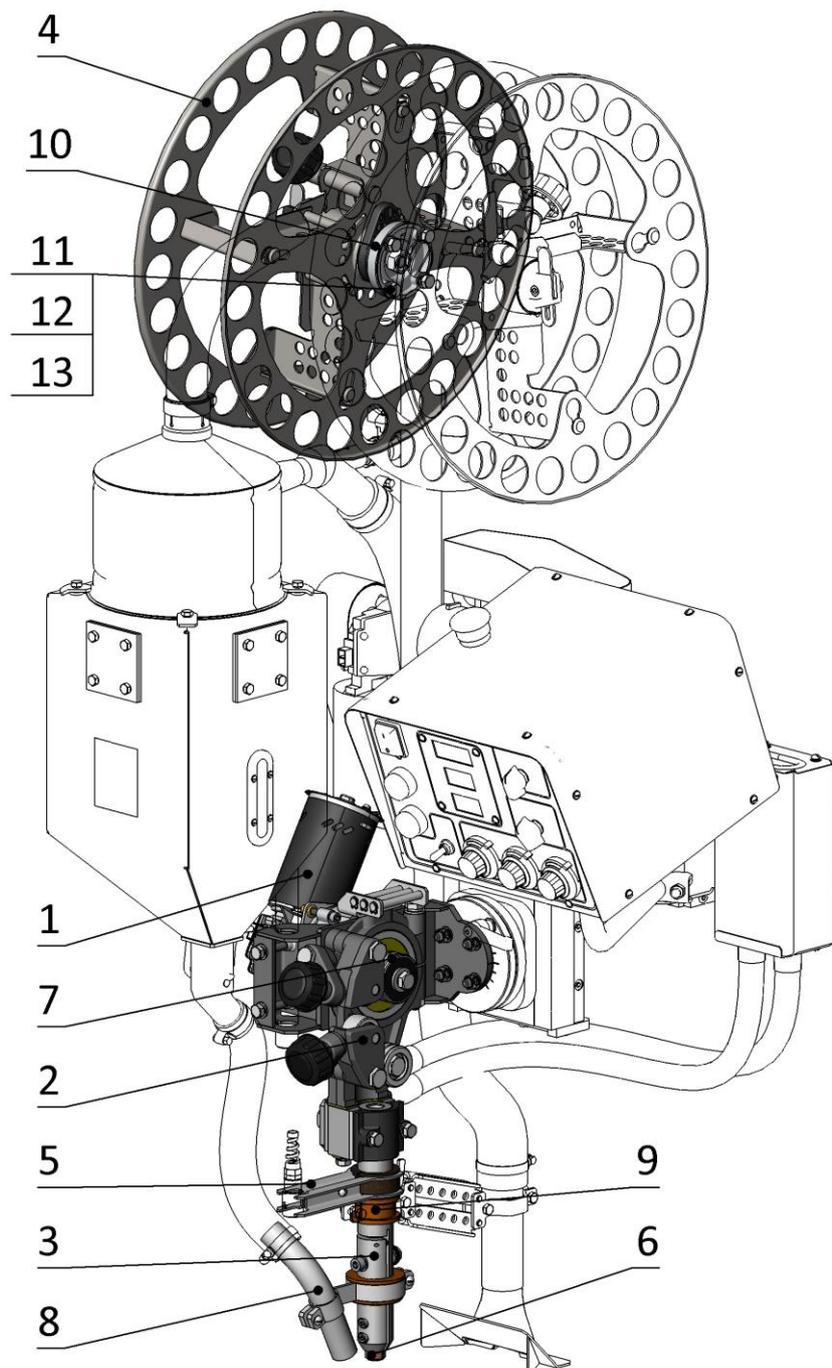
Комплект сварочной головки TWIN max для сварки двумя проволоками $\varnothing 2,4-3,0$ мм.
